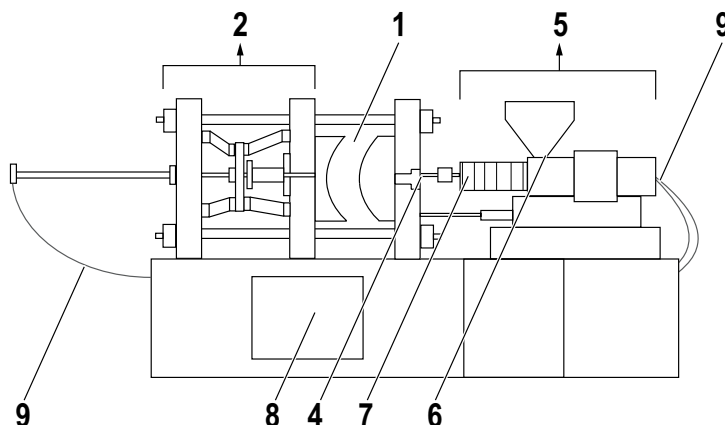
Zonas de peligro de una máquina de moldeo por inyección (vista frontal)
